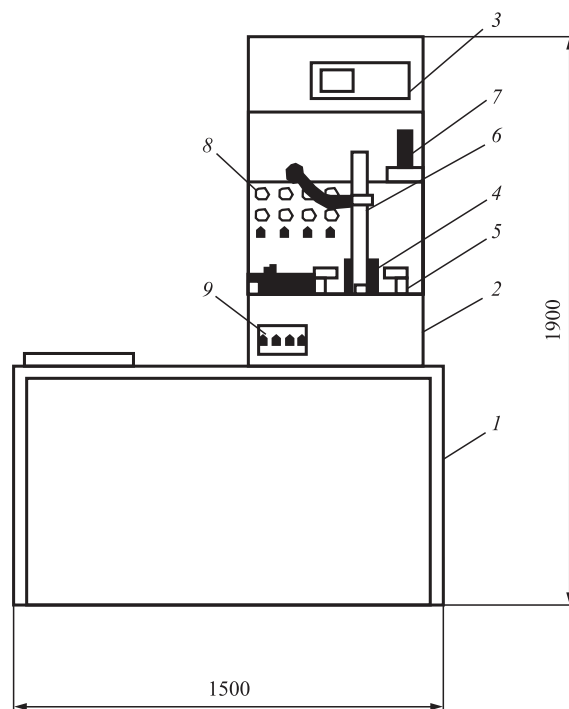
Принципиальная схема станка полуавтоматической заштамповки:
